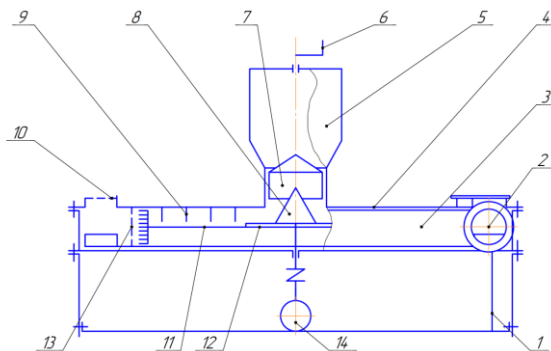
Дробарка зерна: 1 – рама; 2 – патрубок; 3 – робоча камера; 4 – кришка; 5 – бункер; 6 – привід; 7 – обичайка циліндрична; 8 – конус; 9 – штифт; 10 – повітрязабірник; 11 – диск; 12 – кільце магнітне; 13 – решето; 14 – електродвигун.
